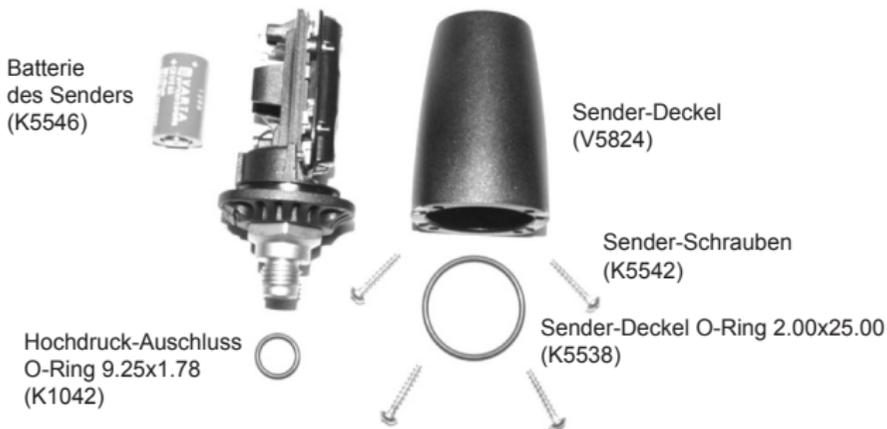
Teile des Drucksenders. Die Zahlencodes bezeichnen die Ersatzteilnummern
